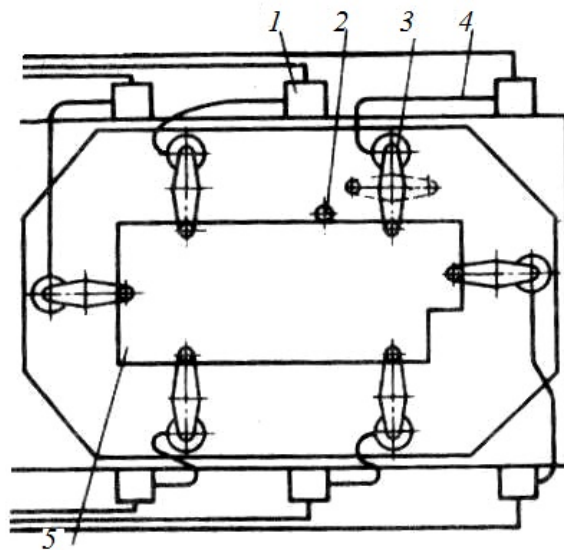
Схема закрепления заготовки с поворотными управляемыми захватами:
